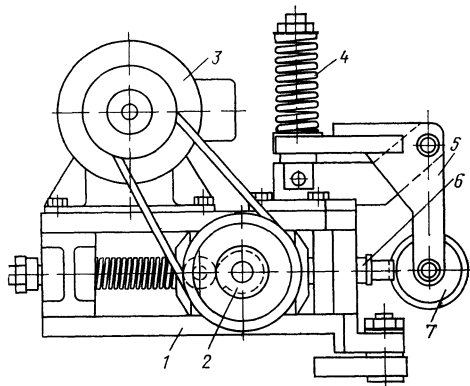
Схема устройства с вибрирующим роликом для образования резьбового профиля
